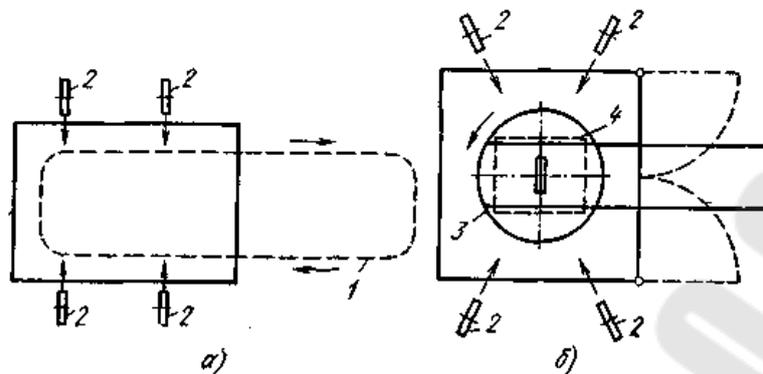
Принципы работы дробеметных камер непрерывного (а) и периодического (б) действия: 1- подвесной конвейер; 2- дробеметные колеса; 3-поворотный круг; 4- тележка
